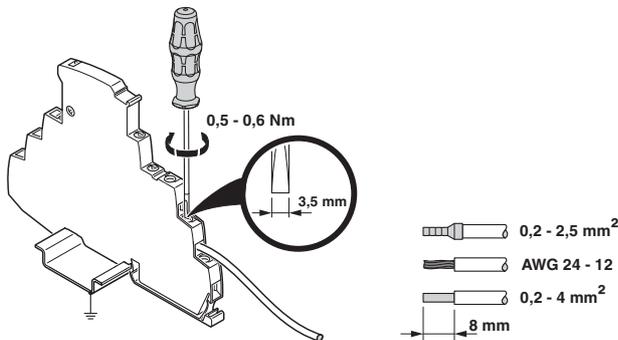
Variante de conexión por tornillo (ancho de construcción 6 mm)
